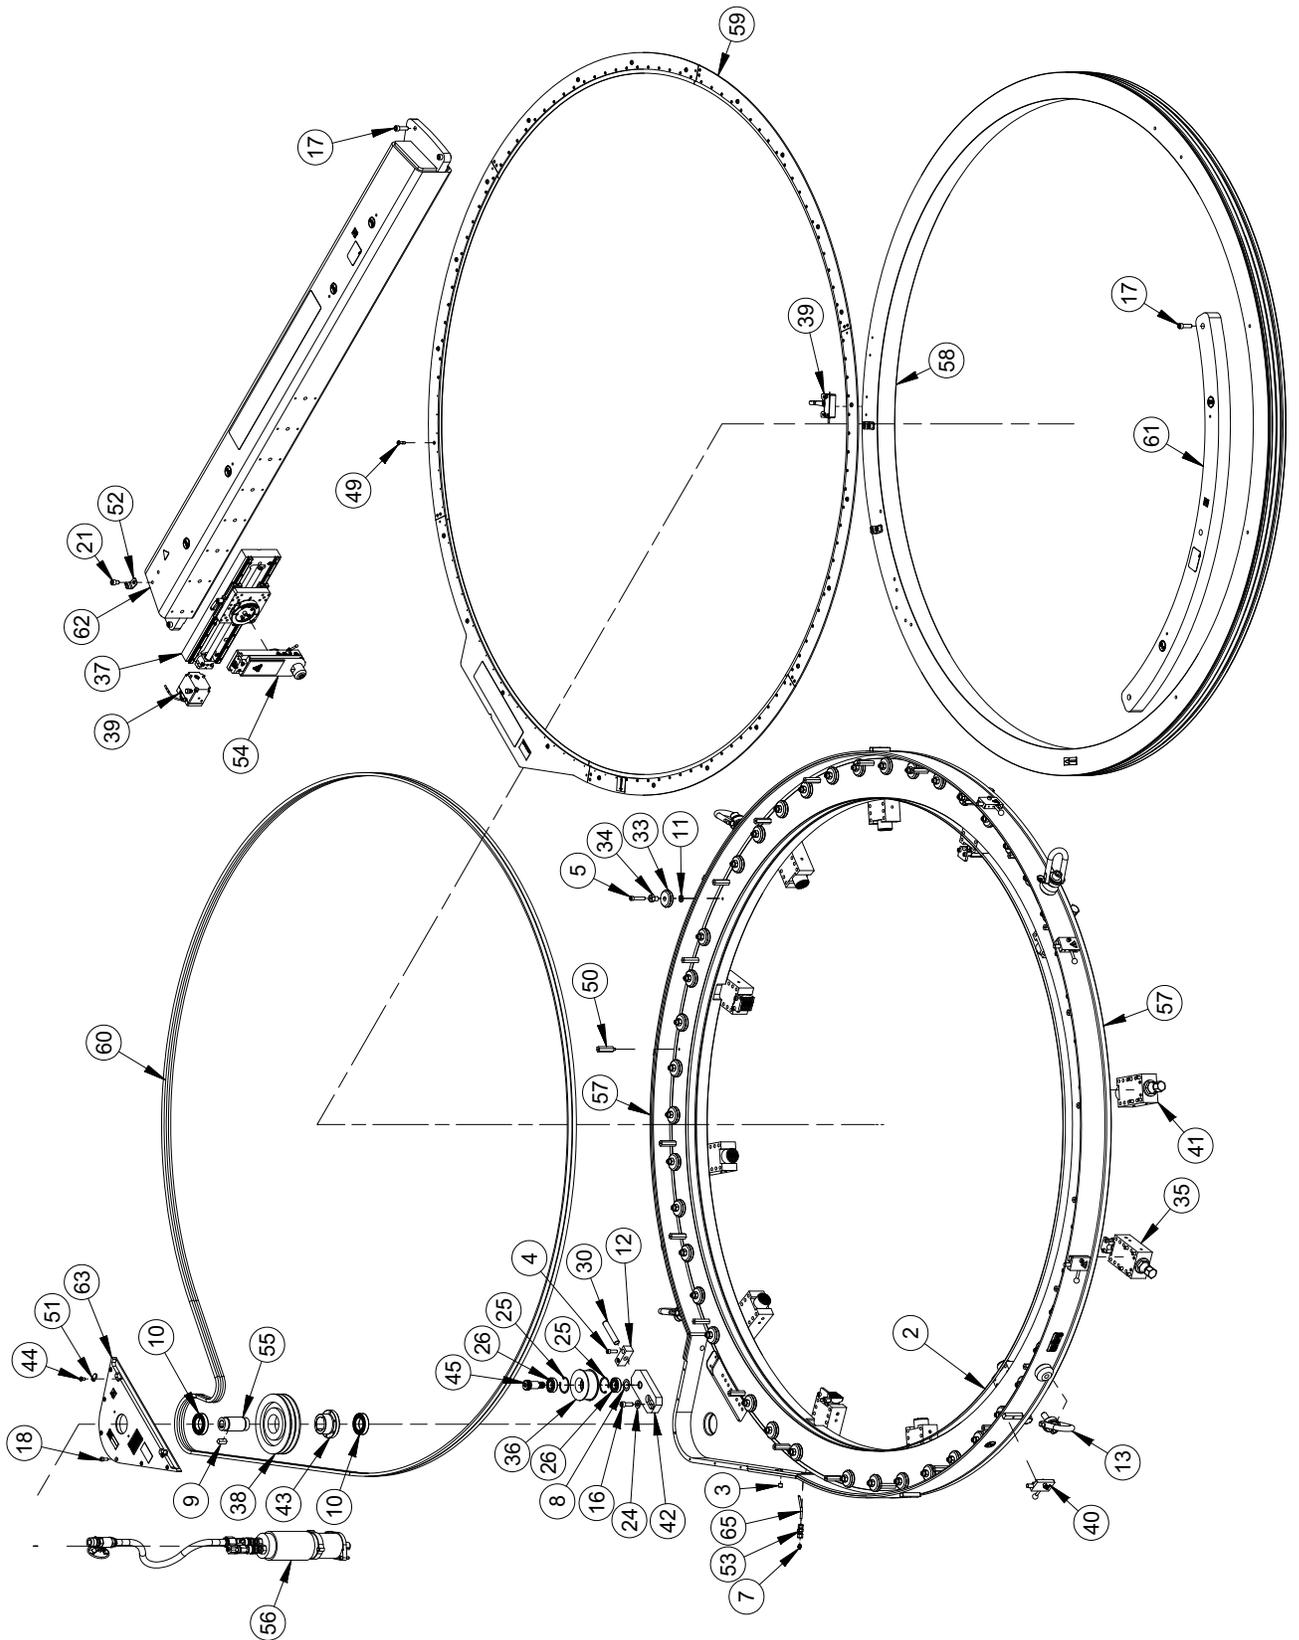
ODF90 SPEED FACER ENSEMBLE 1 (RÉF. 94780)
